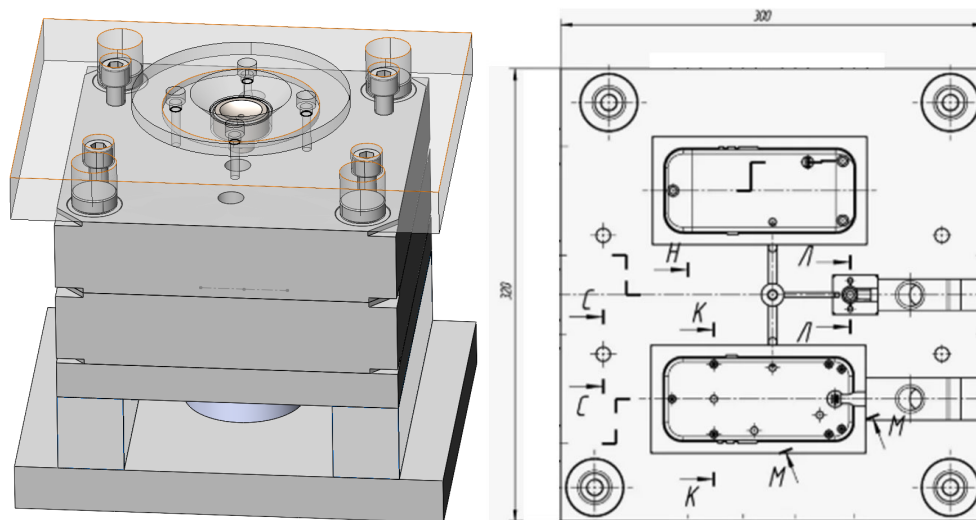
Трехмерная модель двухместной пресс-формы и проекционный вид формообразующей поверхности сборочного чертежа пресс-формы для литья изделия крышка корпуса
